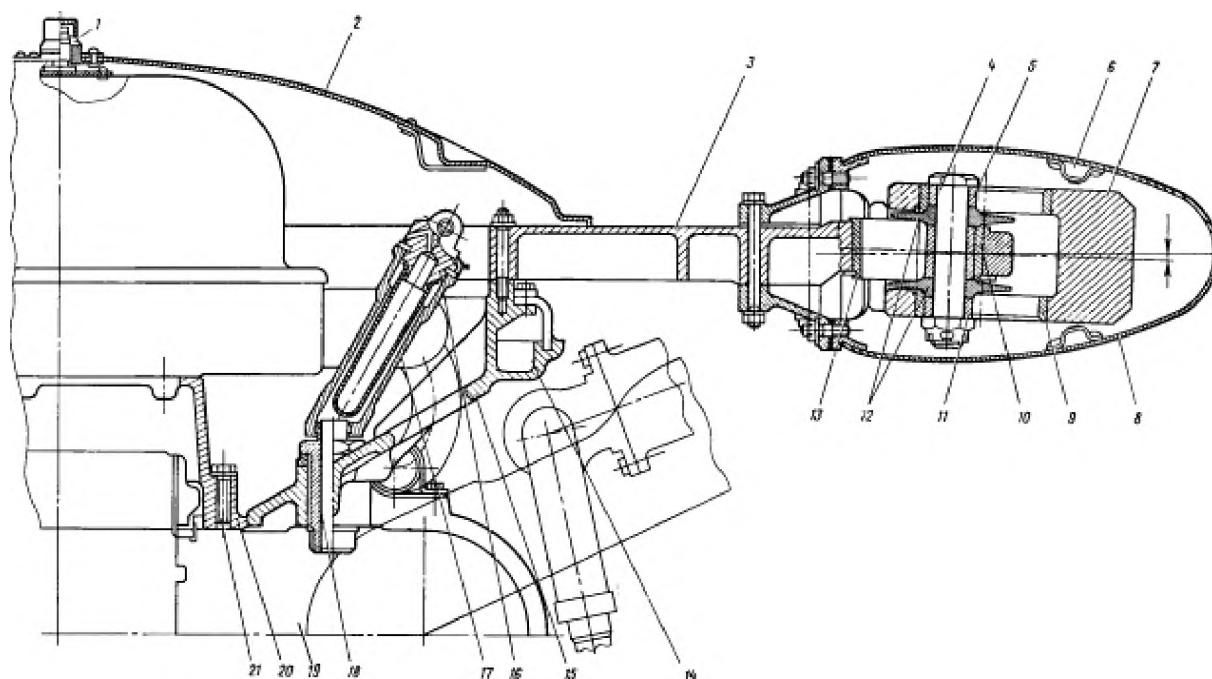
Конструкция бифилярного маятникового гасителя колебаний вертолета Ми-8 [8]:
